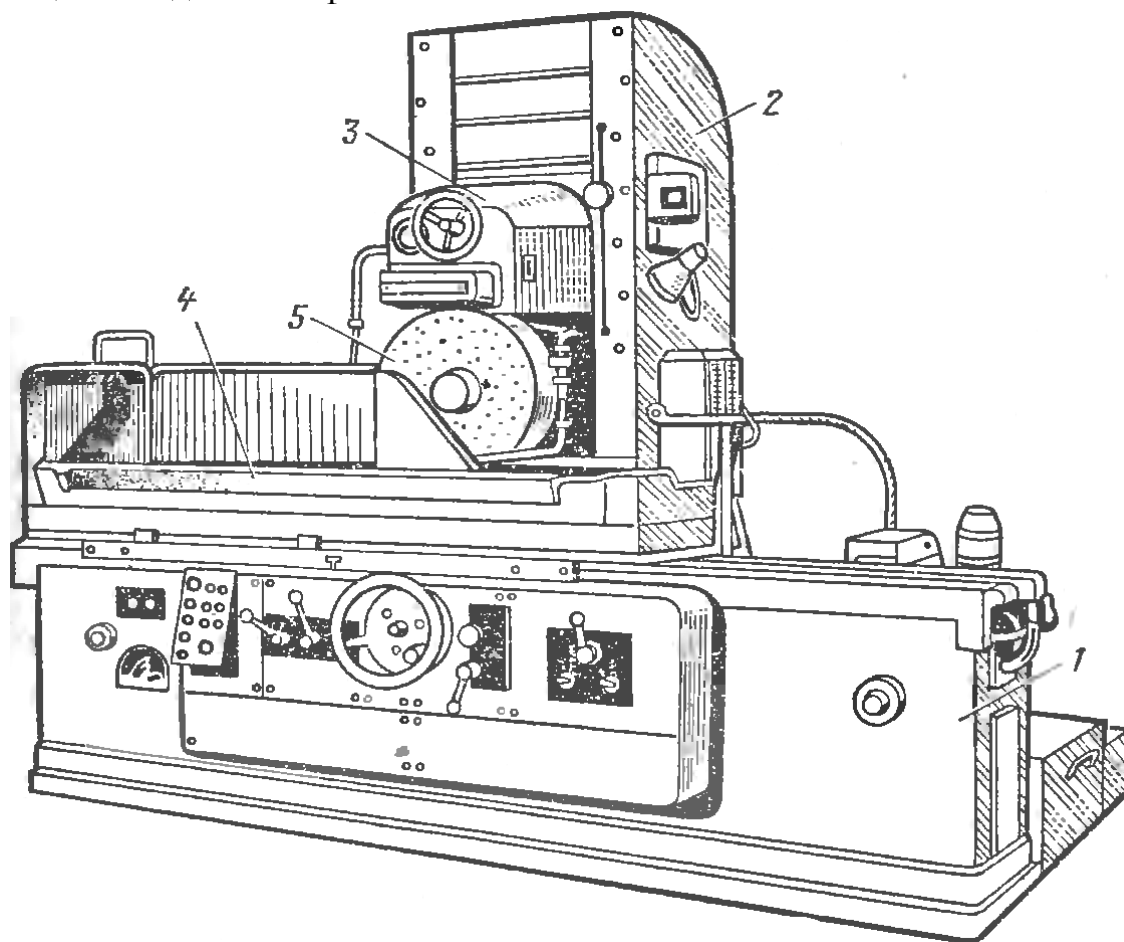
Общий вид плоскошлифовального станка с прямоугольным столом
